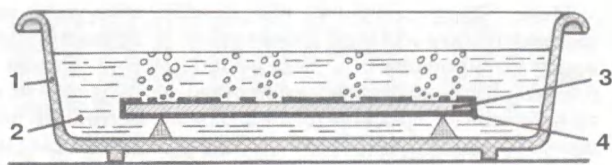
Процесс травления: 1 — кювета; 2 — травитель; 3 — заготовка; 4 — покрывной слой.
